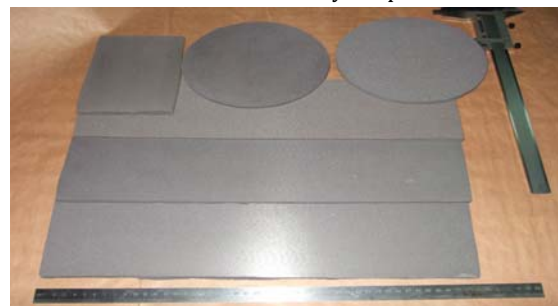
Материалы и изделия, полученные методом сварки и консолидации взрывом
